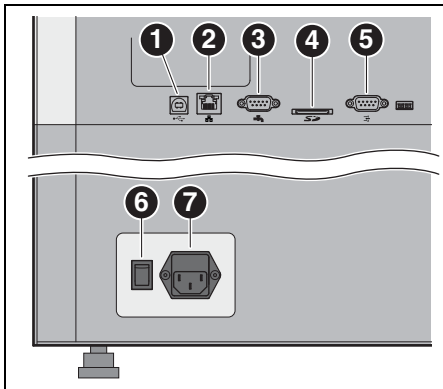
Schnittstellen an der Rückseite der Fräsmaschine
